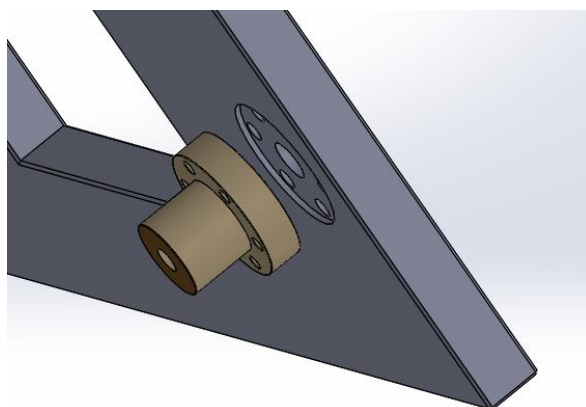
Vista explosionada del conjunto soporte-tuerca-rodamiento
